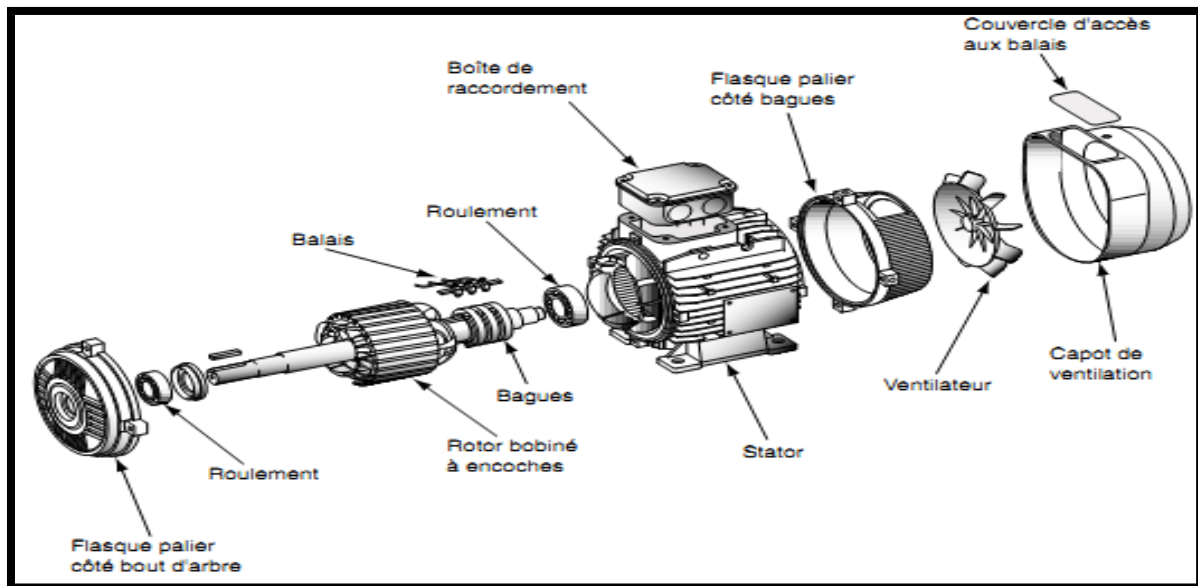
Moteur asynchrone à bague (rotor bobiné).
